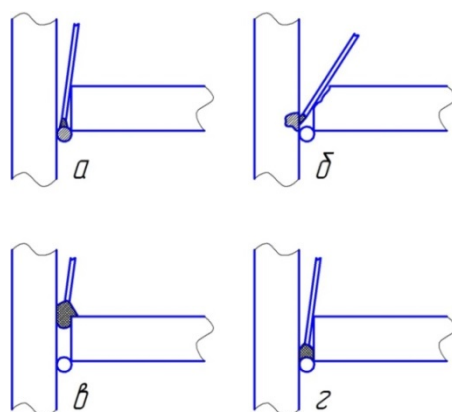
Сварка с остающейся подкладкой в корне шва
